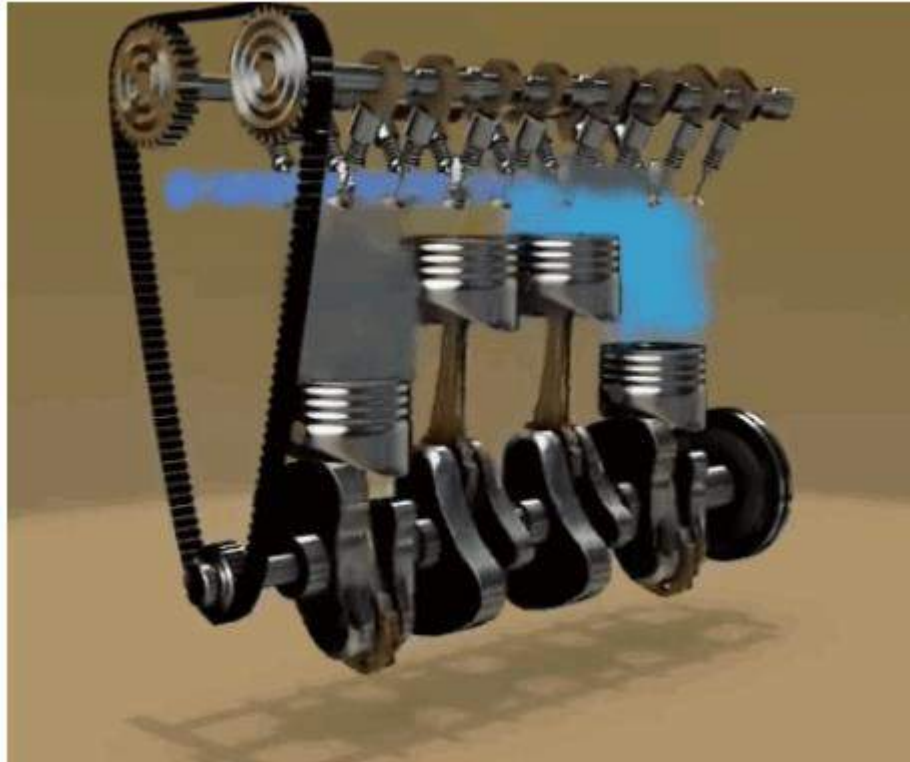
Газорозподільний механізм двигуна MZR Z6
